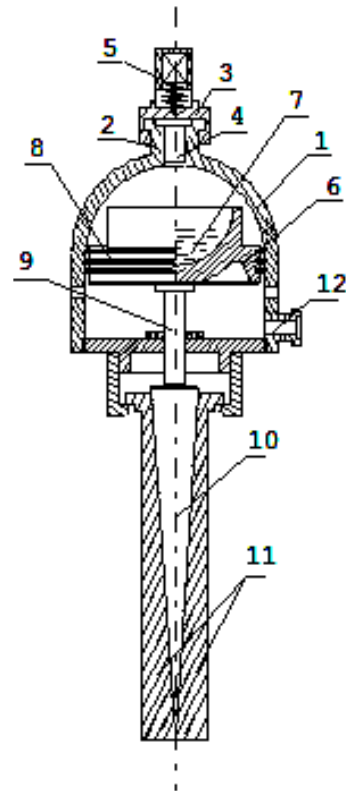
Устрій піроклину: 1 – корпус; 2, 12 – горловини; 3 – затвор; 4 – піропатрон; 5 – ініціатор; 6 – поршень; 7 – горюча рідина; 8 – компресійні кільця; 9 – силовий шток; 10 – розпирний клин; 11 – розсувні щоки
